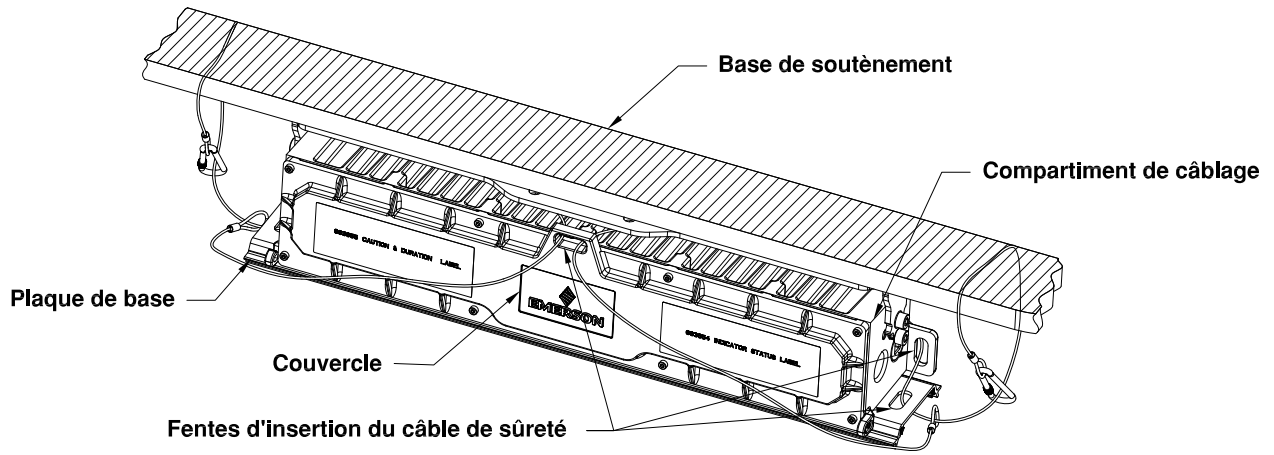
LUMINAIRE RIGMASTER 2 PIEDS AVEC CABLES DE SURETE
